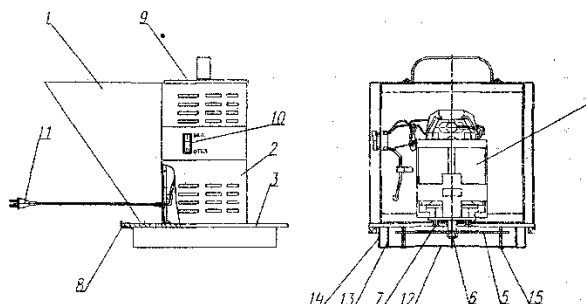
Устройство измельчителя зерна ИЗ-05 (ИЗ-05М)
